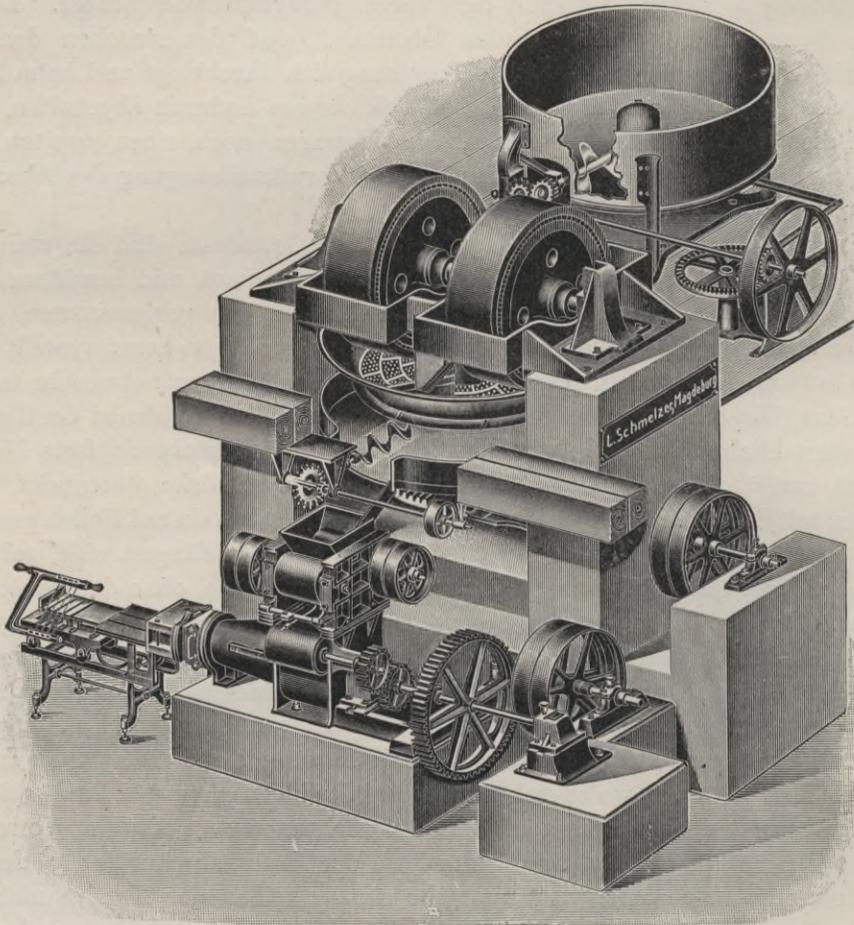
Naßkollergang mit Walzwerk. (*L. Schmelzer-Magdeburg*.)
